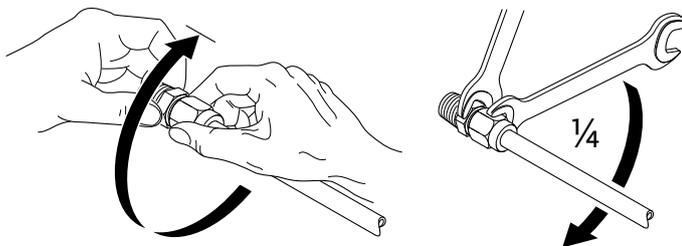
1/4 de rotação adicional da abraçadeira de ligação
